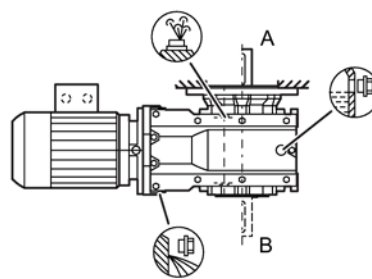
Монтажные положения для конического редуктора В.Ф в исполнении с фланцем и В.З с фланцем корпуса, типоразмеры 39–49
